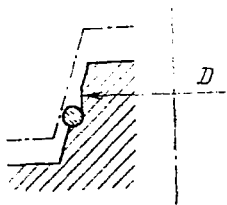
Схема конического соединения с проволочным уплотнителем.
